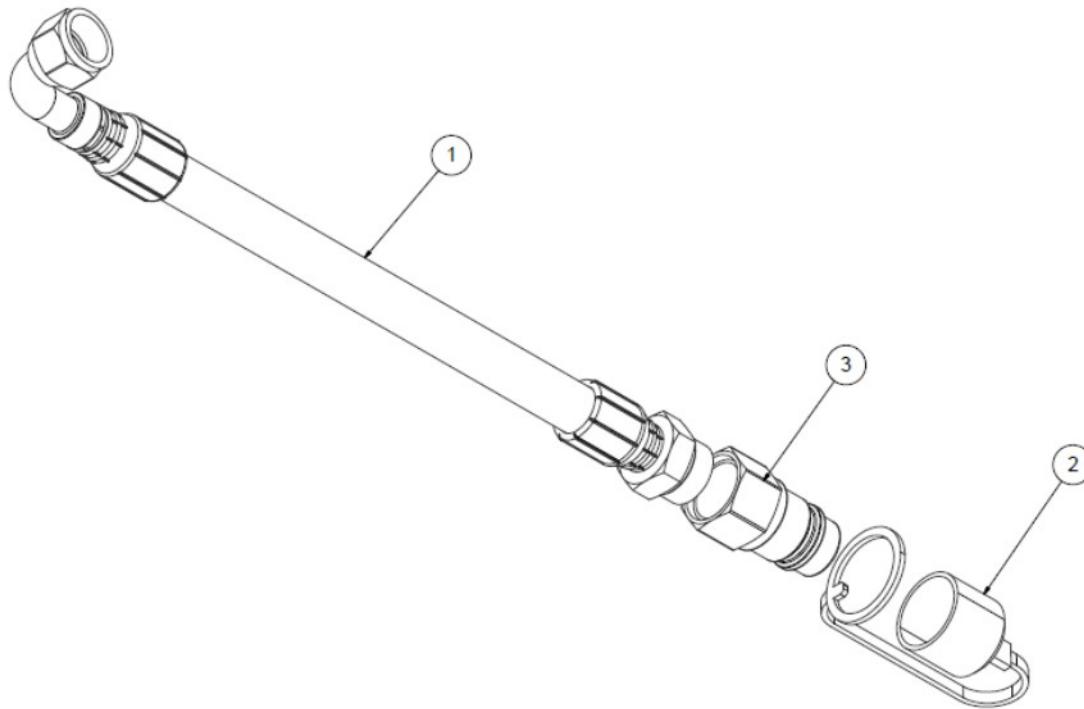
Чертеж сборки шланга гидравлического цилиндра опрокидывания кузова - втягивание – 815612
